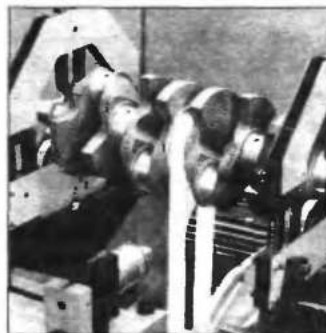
Станок для динамической балансировки коленчатых валов
